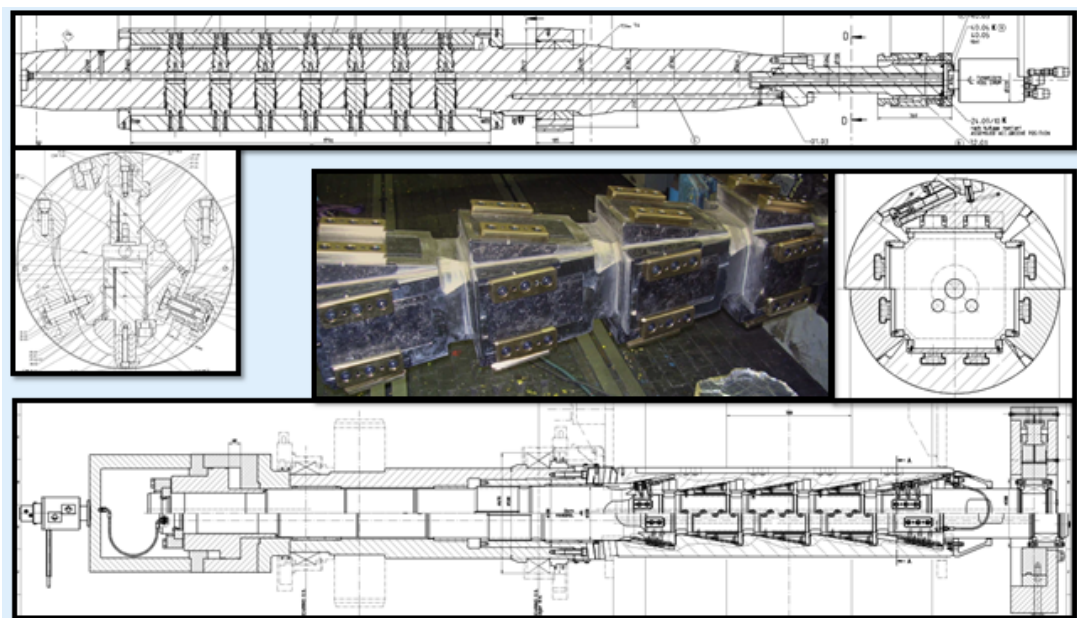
Desenho de conjunto geral e foto de um mandril de laminador a frio reversível.
